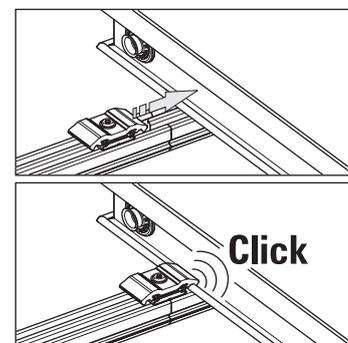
Posizionare la piastrina di bloccaggio doppia
